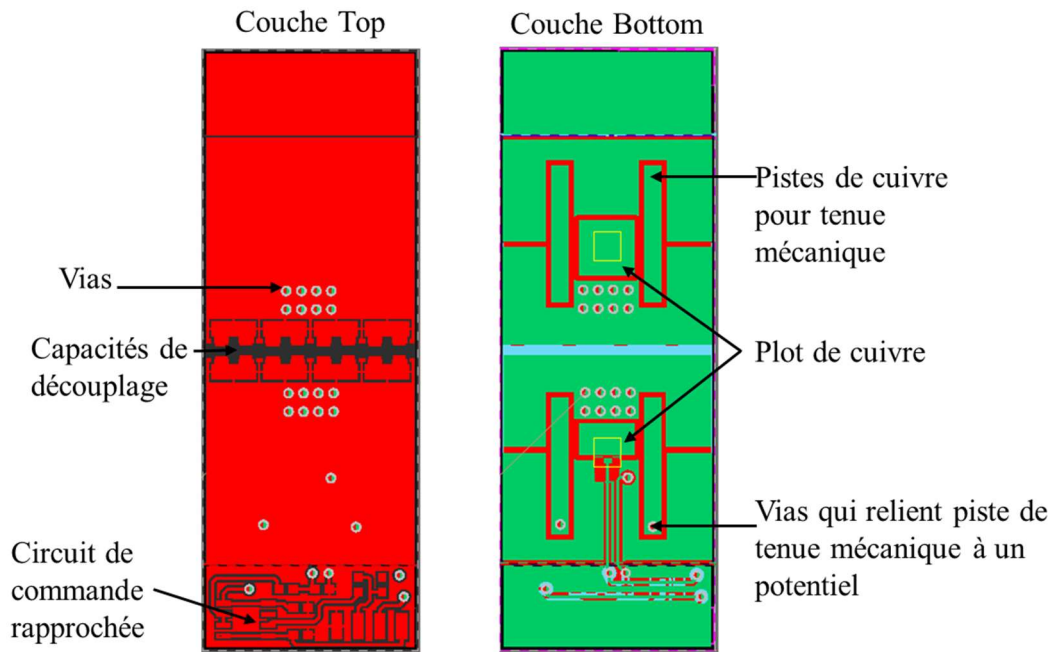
2 : PCB 1 cellule de commutation avec PCB et bumps
